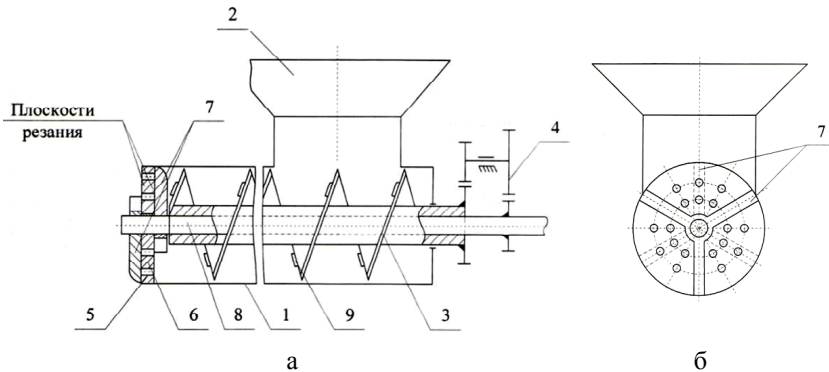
Схема измельчителя коры: а – вид спереди; б – вид слева
